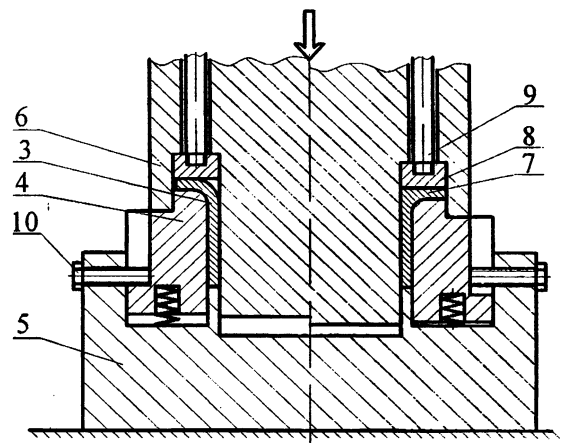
Схема штампа формоизменения торообразного участка заготовки
